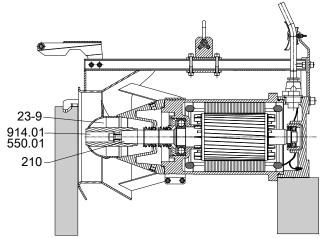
Desmontaje de la hélice axial; Amaline 300 con motor 8 6
